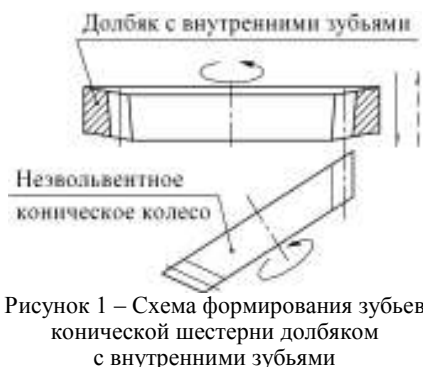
Схема формирования зубьев конической шестерни долбяком с внутренними зубьями
